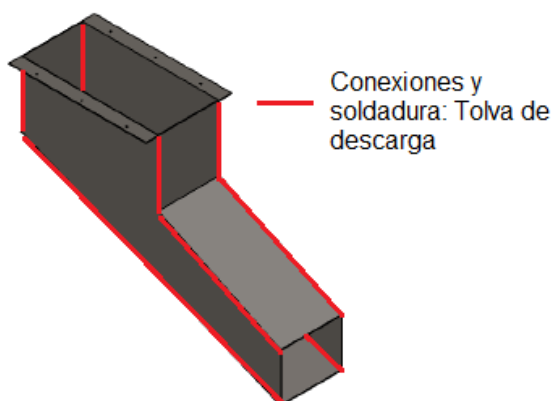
Conexiones y soldadura tolva de descarga.
